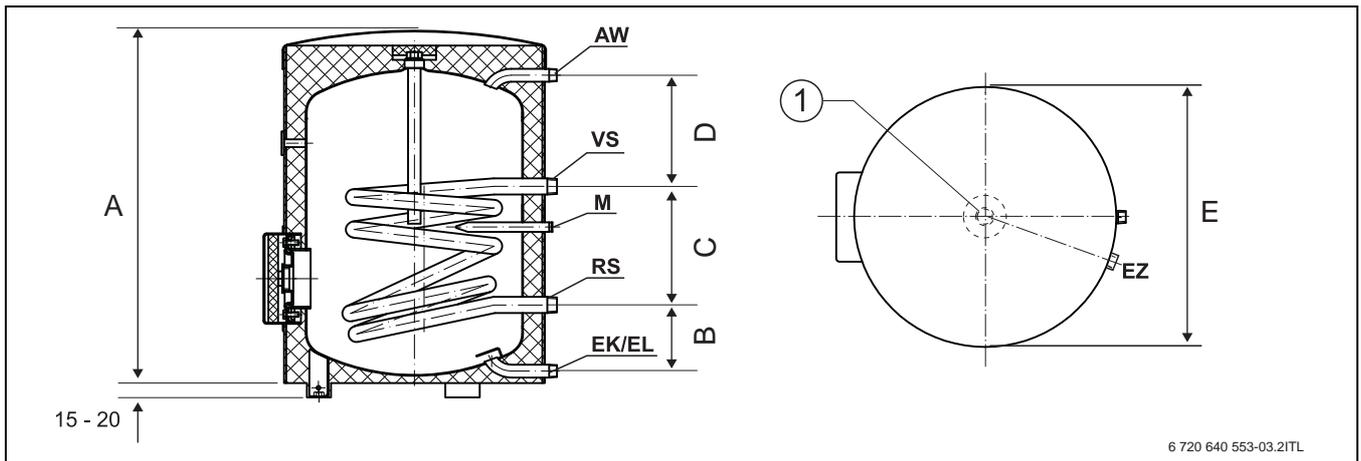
Dimensiones y conexiones Storacell S75-90 ZB-solar
